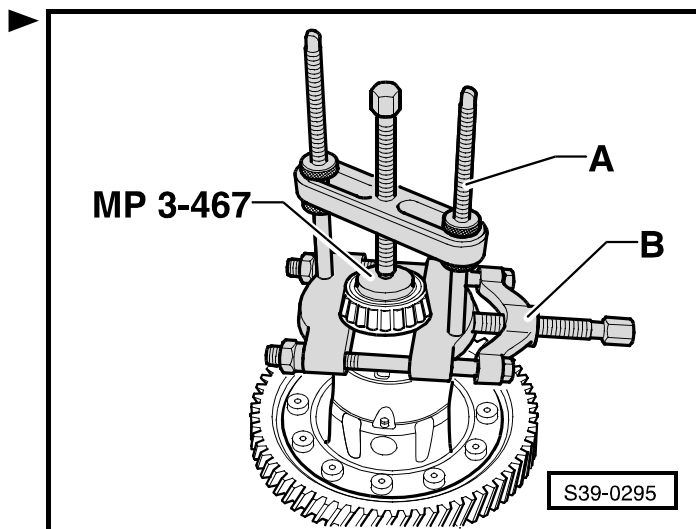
Запрессовывание внутреннего кольца конического роликоподшипника
